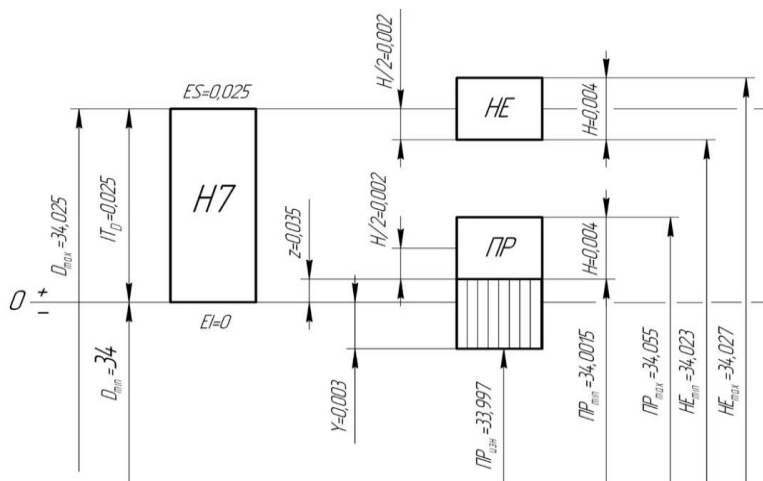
Допуск калибра для контроля отверстия
